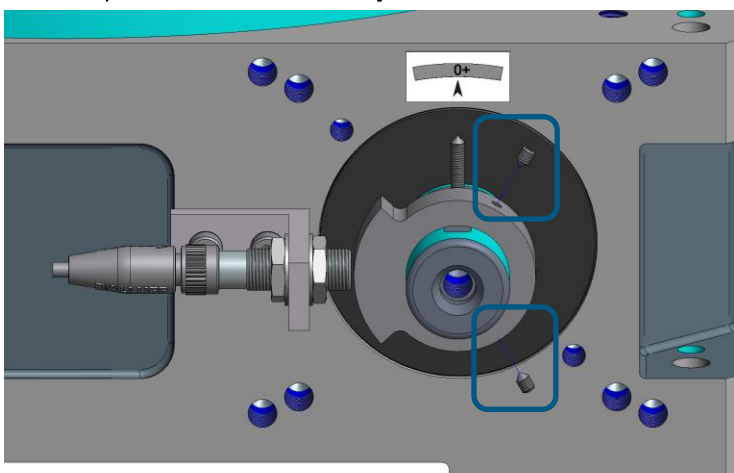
Detalle: Leva de posicionamiento desmontaje tornillos
